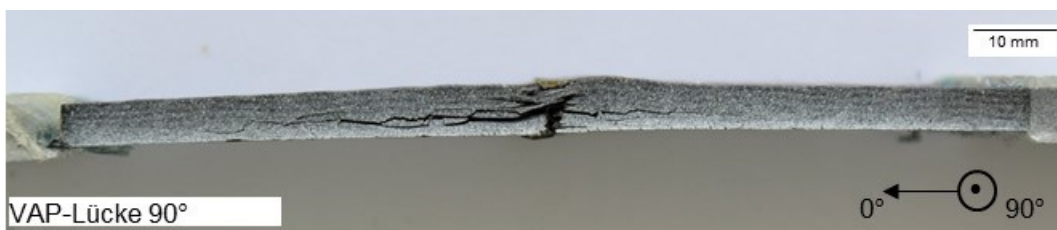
Bruchbild einer VAP-Lücke 90° -Zugprobe
